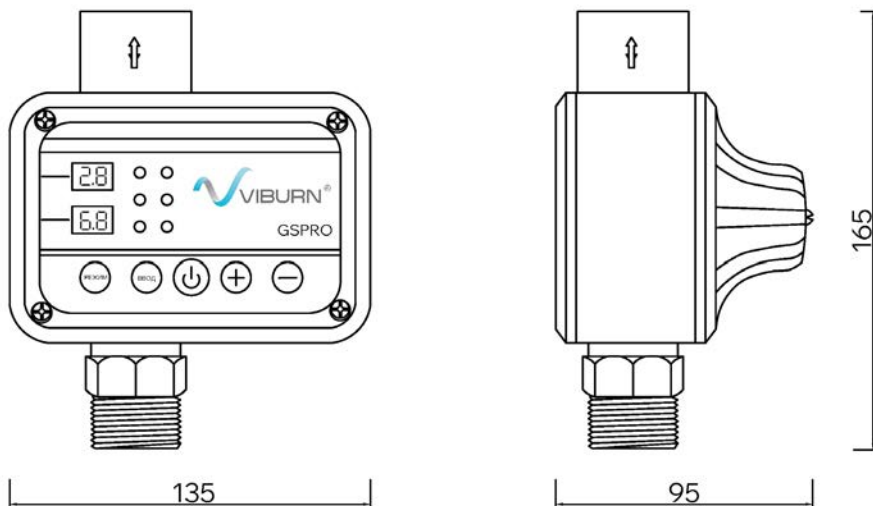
Габаритные и присоединительные размеры GSPRO
